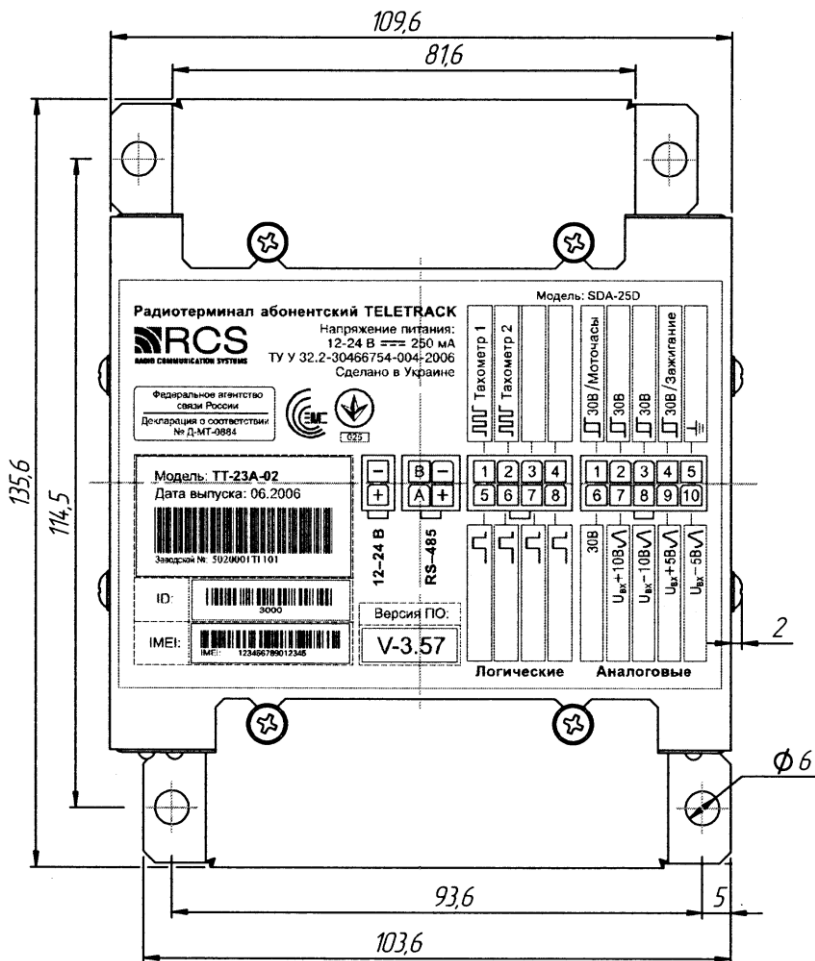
Вид сверху, габаритные размеры и крепежные отверстия корпуса абонентского радиотерминала Teletrack.
